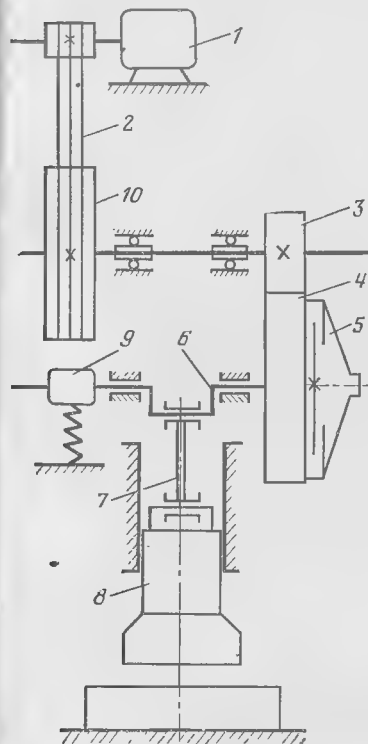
Кинематическая схема механического кривошипного ковочно-штамповочного прес-са.
